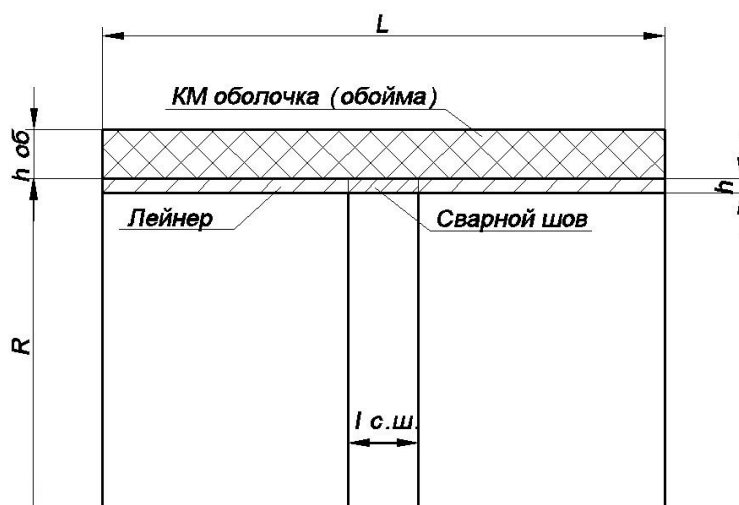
Представительный элемент цилиндрической части МК БВД
